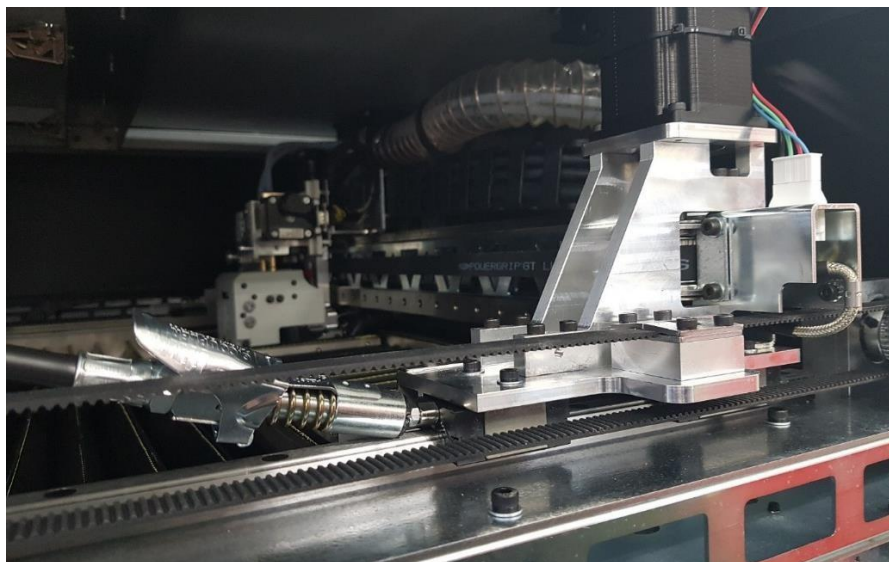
Подача смазки в смазочные ниппели в правой части принтера
